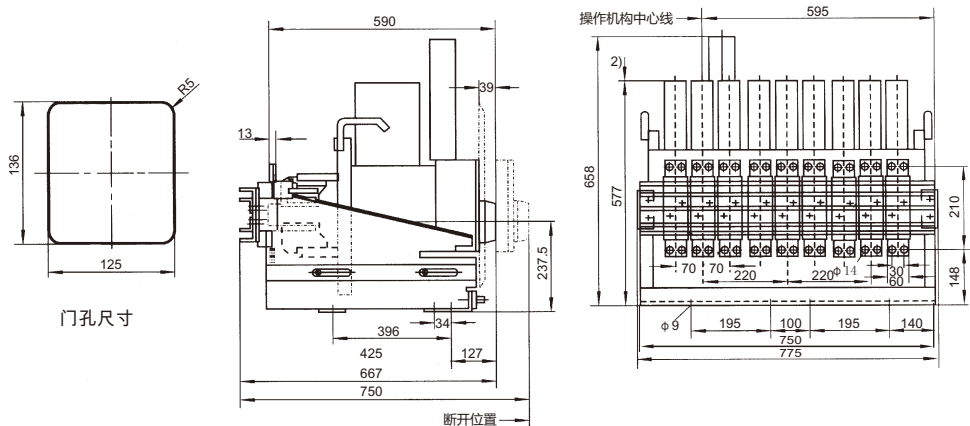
DW17D-3900(In=3900A)抽屜式断路器外形尺寸和安装尺寸
